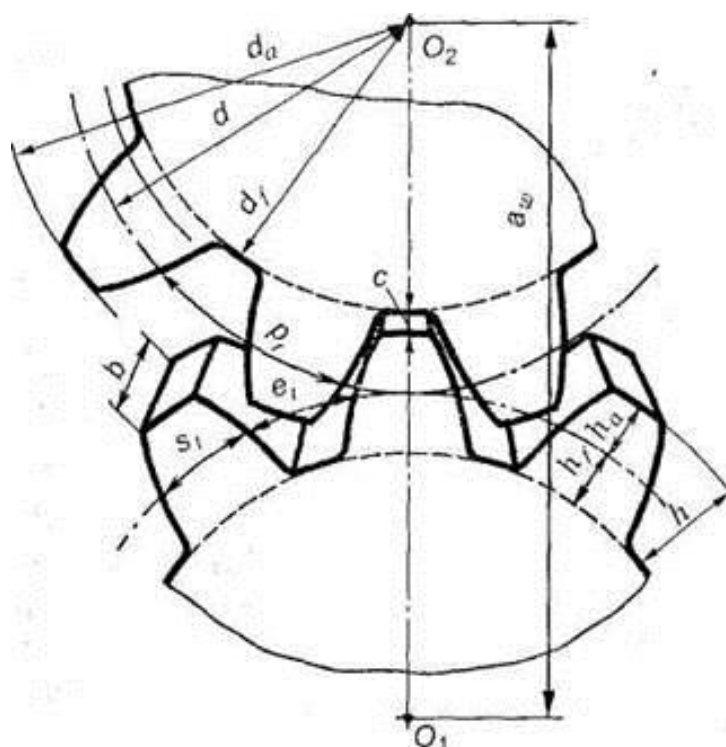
Геометрические параметры цилиндрических зубчатых колес
